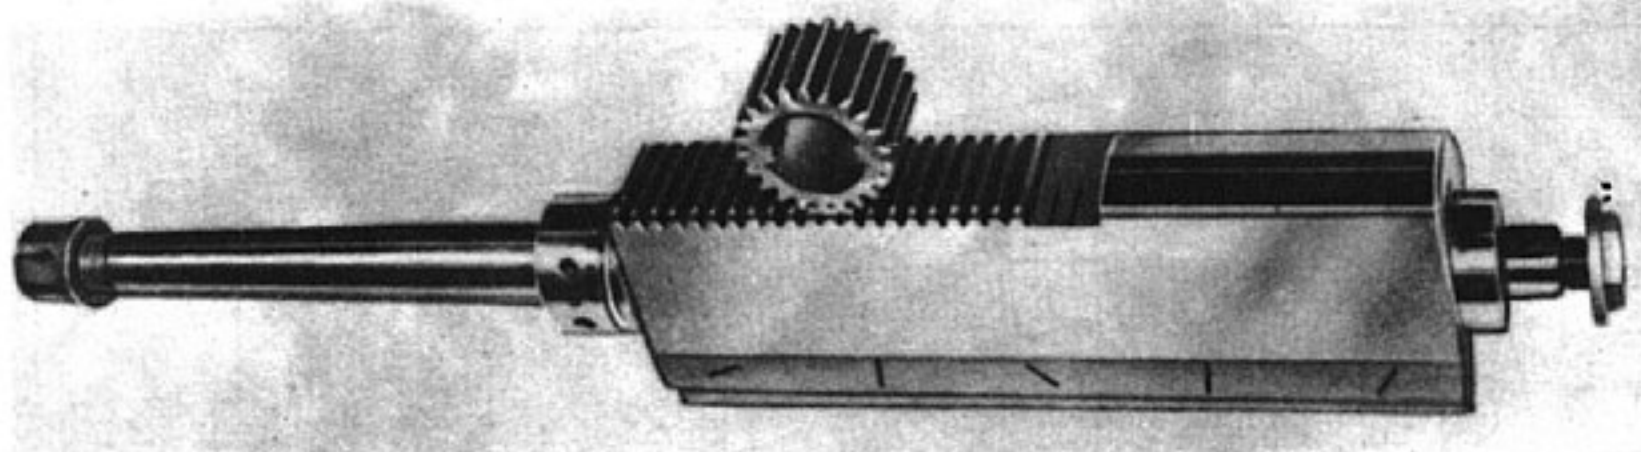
Piñón y cremallera. (The Fellows Gear Shaper Company.)
